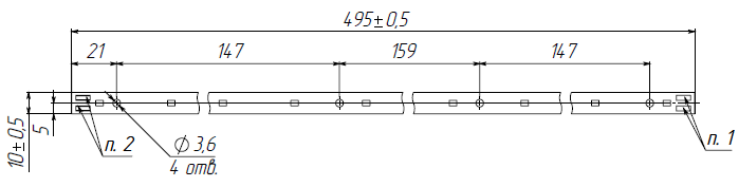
Внешний вид с габаритными и присоединительными размерами СДПП серии FLASH+
